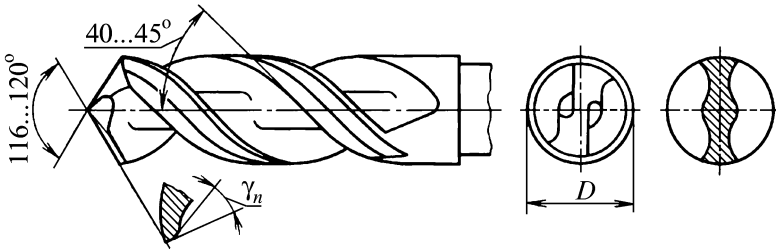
Сверло для обработки труднообрабатываемых материалов
